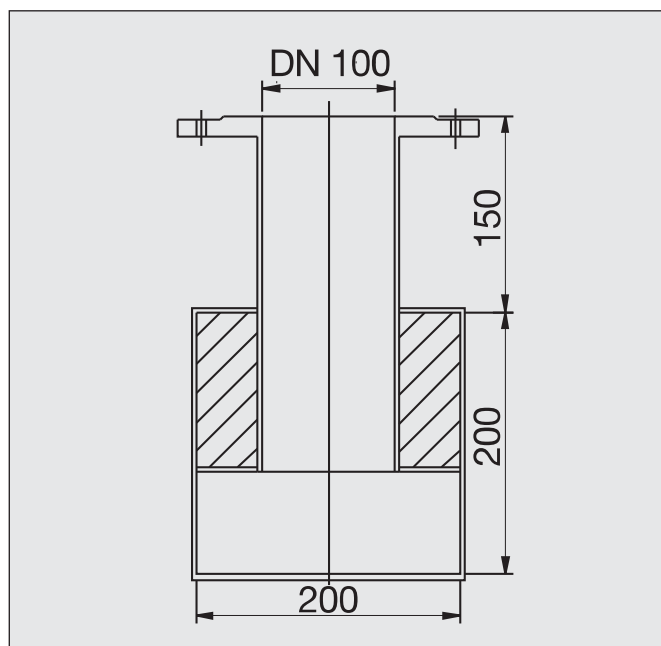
Hrdla přírub v jedné rovině, standardní délky 150mm
